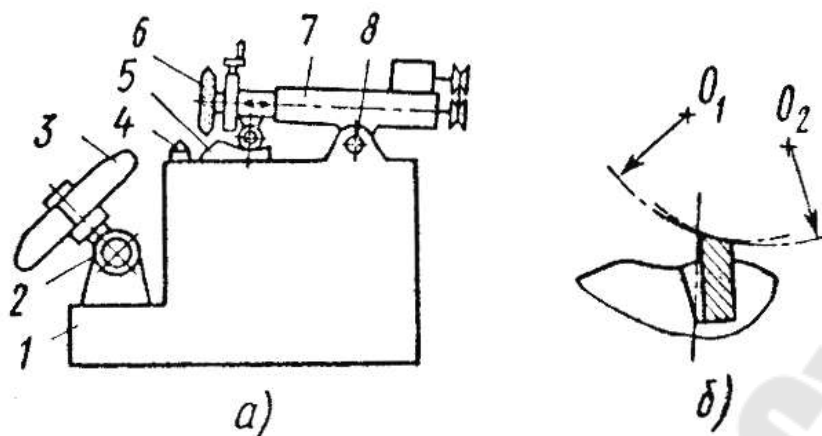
Компоновка полуавтомата модели ВЗ-152Φ2 (а) и схема заточки задней поверхности торцевой фрезы (б): 1 – станина; 2 – ось наклона бабки изделия; 3 – фреза; 4 – алмаз; 5 – копир; 6 – абразивный инструмент; 7 – шлифовальная бабка; 8 – ось качания шлифовальной бабки;  $O_1$ ,  $O_2$  – положение оси абразивного инструмента при заточке по пластине и по державке
